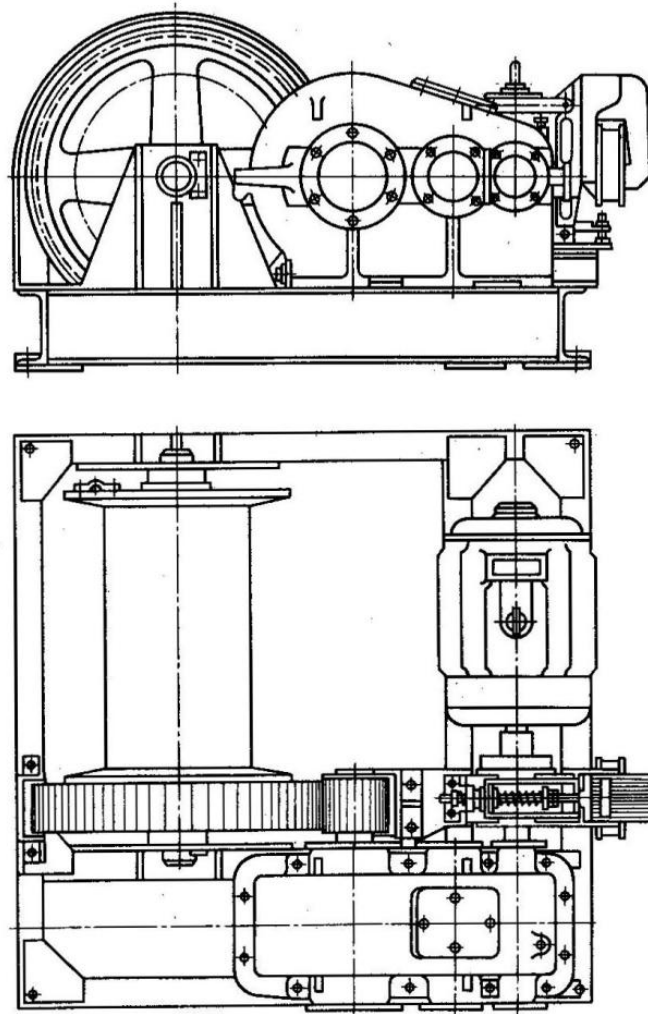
Сборочный чертеж лебедки с дополнительной открытой передачей
